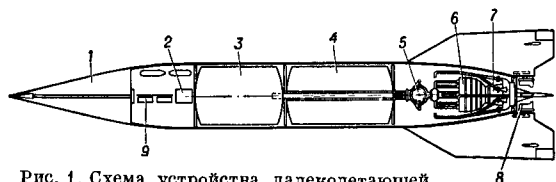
Схема устройства далеколетающей ракеты на жидком топливе: 1 — боевая часть; 2 — автопилот; 3 — бак с горючим; 4 — бак с окислителем; 5 — турбонасосная установка; 6 — камера сгорания; 7 — сопло; 8 — газовые рули; 9 — отсек радиооборудования.
